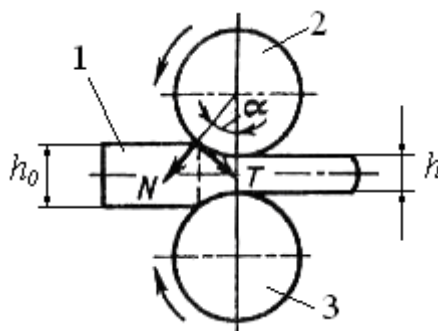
Схема прокатування металу: 1 – заготовка; 2, 3 – валки; h_0 – початкова і h – кінцева висота заготовки; α – кут захоплення
